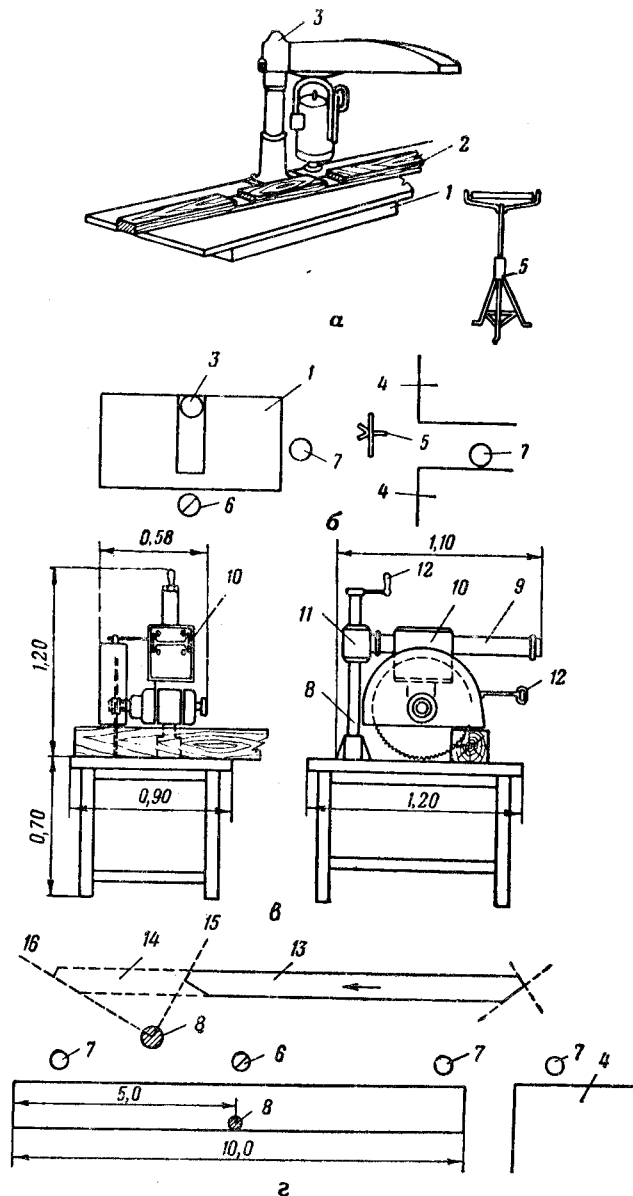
Выборка врубок станком УДП и торцовочным станком Зернова и Карасева:
